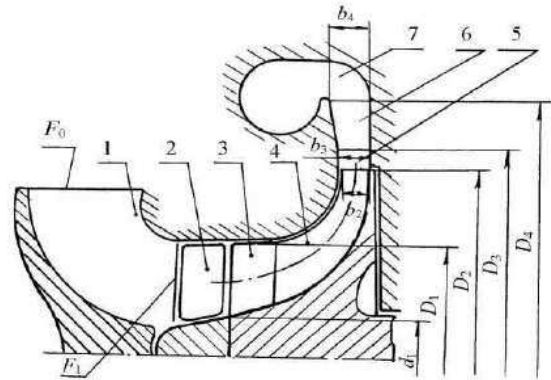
Схема проточної частини відцентрового компресора [7]:
